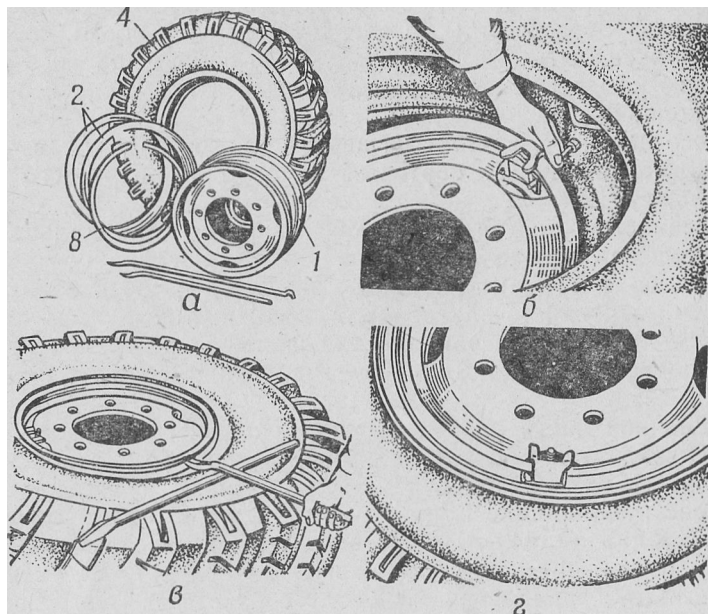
Приемы сборки колеса с шиной (обозначения см. рис. 59)
